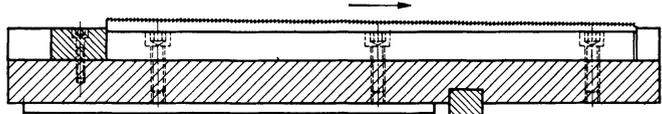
Befestigung des Schneideteils auf dem Werkzeughalter und Aufnahme der Schnittkraft durch Querriegel.
